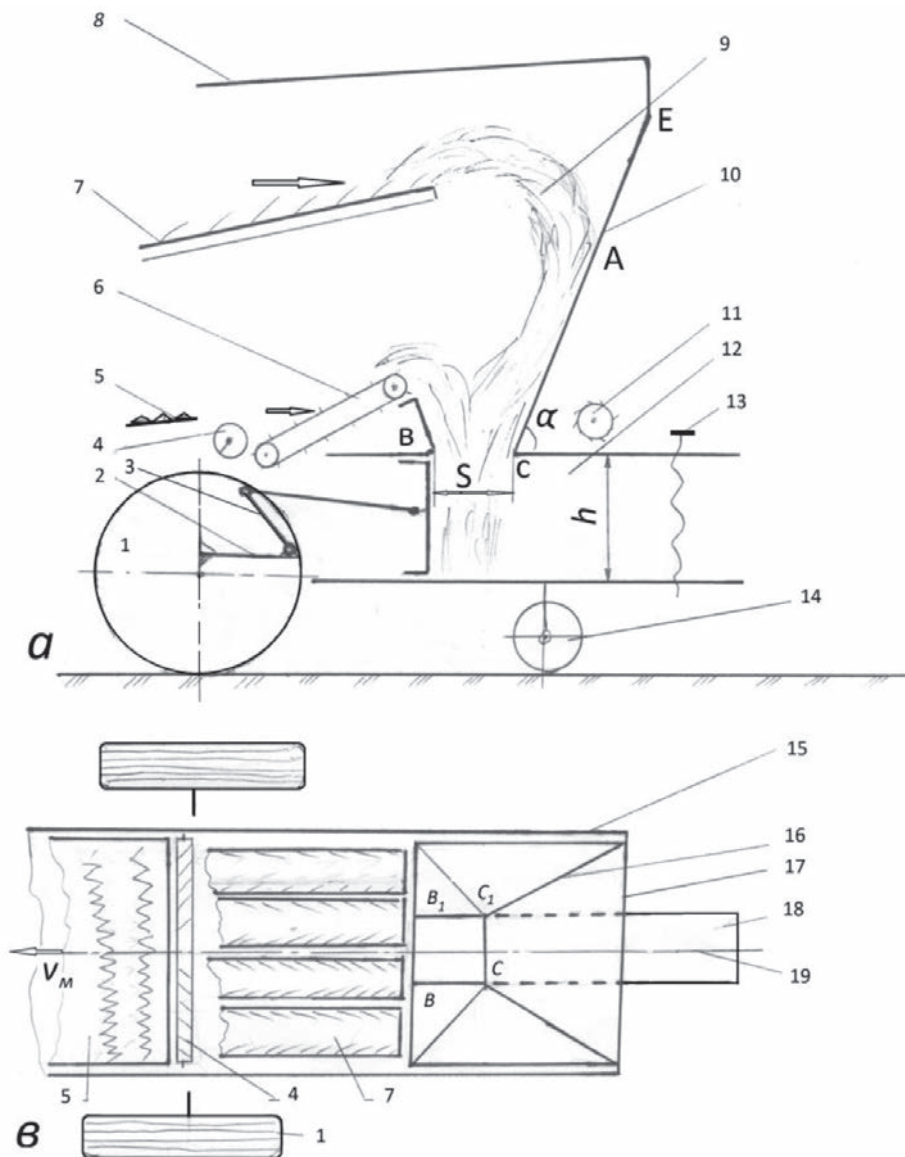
Схема установки соломопрессующего аппарата вместо соломоизмельчителя и разбрасывателя на комбайн Dominator 130: *a* – вид сбоку; *б* – вид сверху; 1 – заднее колесо комбайна; 2 – балка для крепления соломоизмельчающего и разбрасывающего устройств; 3 – кривошип привода соломопрессующего поршня; 4 – шнек для транспортировки половы мелких примесей, сходящих с верхнего решета; 5 – верхнее решето; 6 – ленточный транспортер; 7 – клавиша соломотряса; 8 – крыша комбайна; 9 – траектория схода соломы с соломотряса; 10 – щиток-направитель; 11 – привод вязального аппарата; 12 – прессовальная камера; 13 – регулятор плотности тюков; 14 – опорное колесо тележки прессующего аппарата; 15 – боковина комбайна; 16 – щиток-направитель; 17 – задний щиток; 18 – сход с соломопрессующего аппарата; 19 – ось симметрии комбайна
